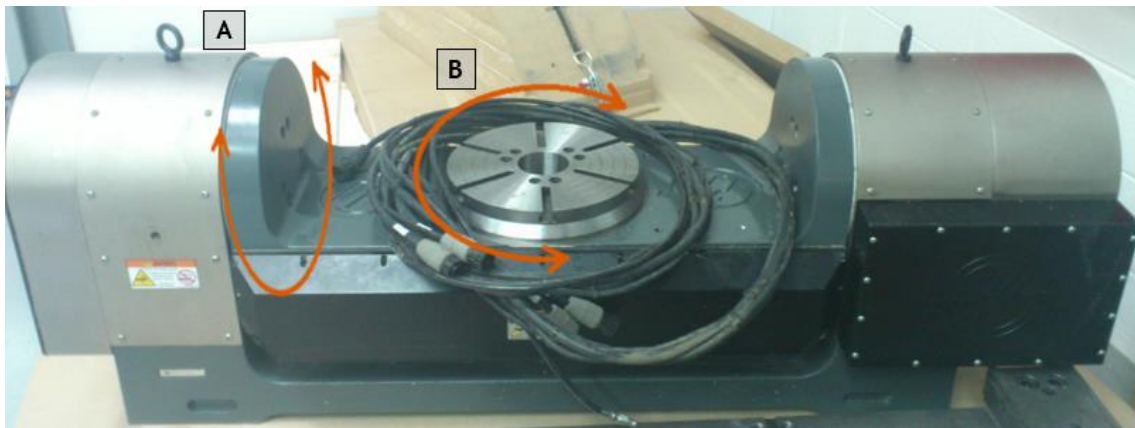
Prato divisor (modelo Haas TR310) que é montado no centro de maquinagem; a direção aproximada dos eixos A e B está também representada na figura.
